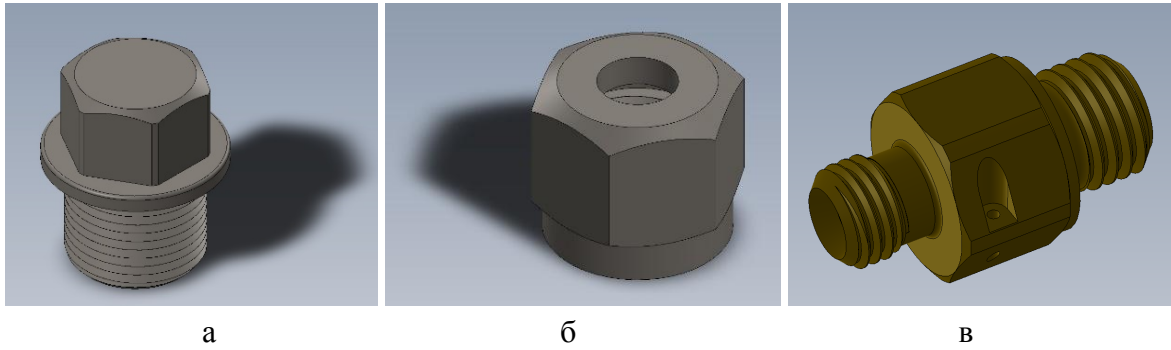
Приклади деталей: а – накривка; б – гайка накидна; в – штуцер
